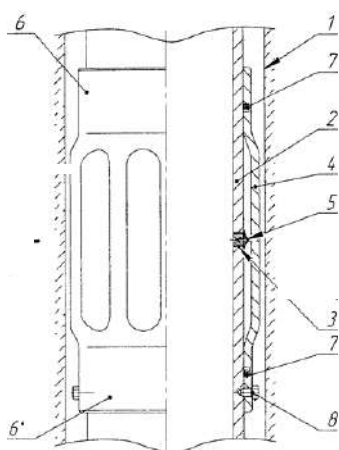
Центратор гидравлический [7]: 1 – ствол скважины; 2 – корпус; 3 – радиальные каналы; 4 – центрирующие элементы; 5 – средство перевода центрирующих элементов в рабочее положение; 6 – гофрированные трубы с кольцевыми зауженными каналами; 7 – самоуплотняющиеся манжеты; 8 – винты
